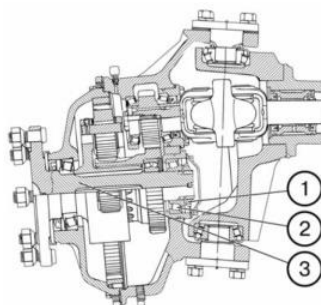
Проверка зазоров в подшипниках передних колес
